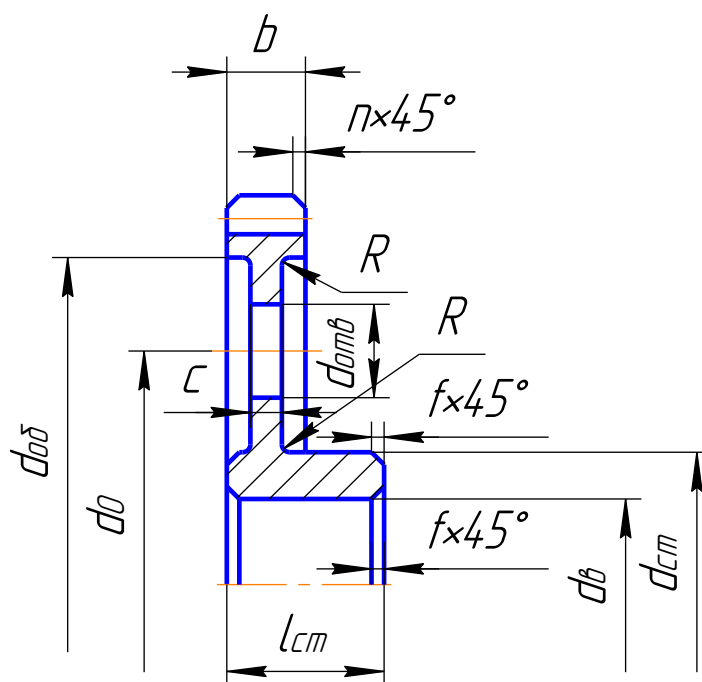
Конструкция и размеры зубчатых цилиндрических колес
